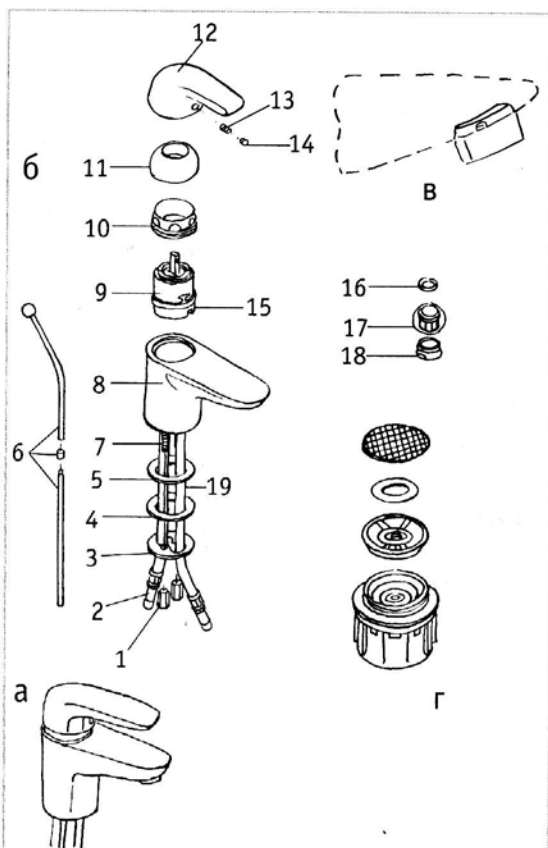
Однорычажный смеситель с запорным шаром в картридже серии «Метрис» фирмы «Хансгроз»: а — в сборе; б — детализовка; в — аэратор в сборе; г — детализовка аэратора;
